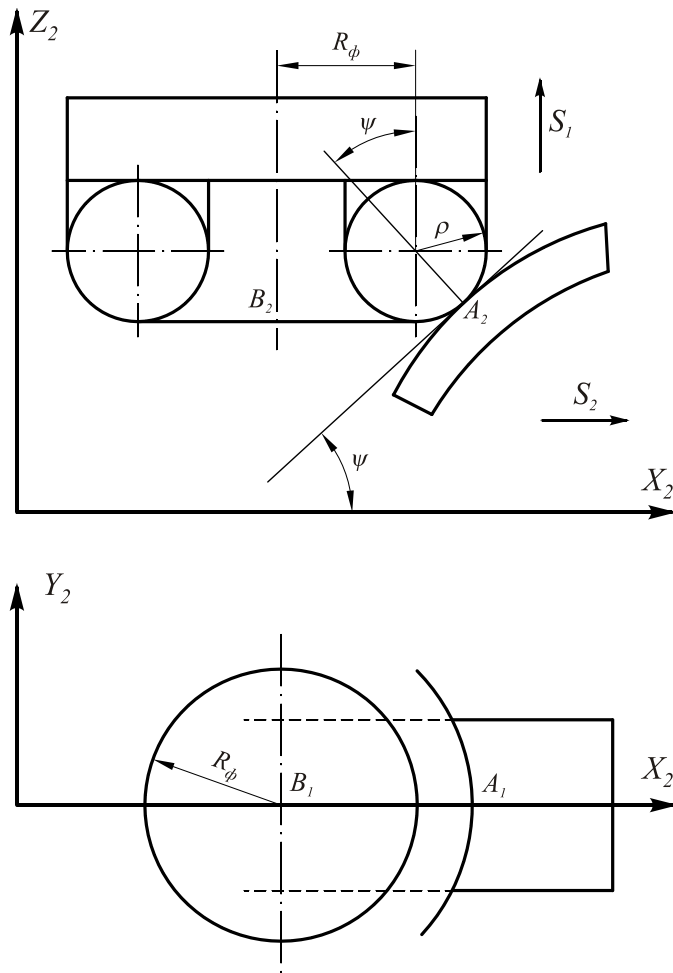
Схема обробки торцевою фрезою, оснащеною круглими пластинами
